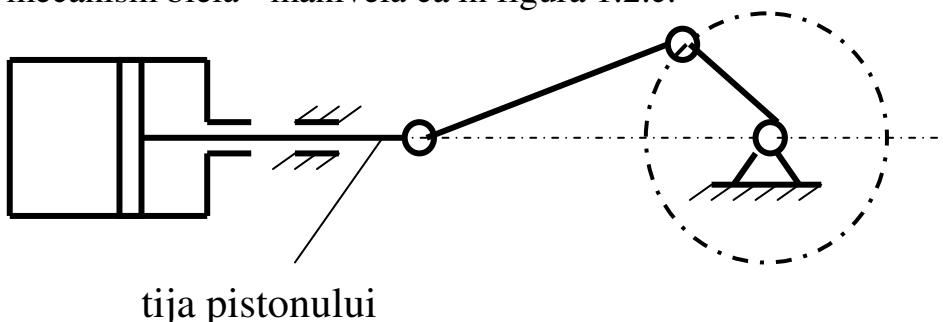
c Întindere și compresiune centrică în tija pistonului
